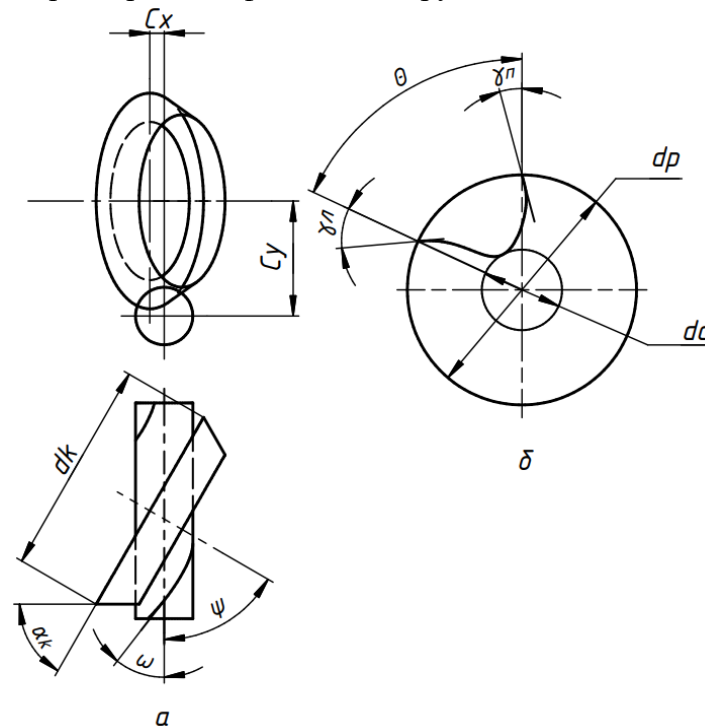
Схема получения канавки фрезы. а – положение круга при шлифовании, б – получаемая канавка.
